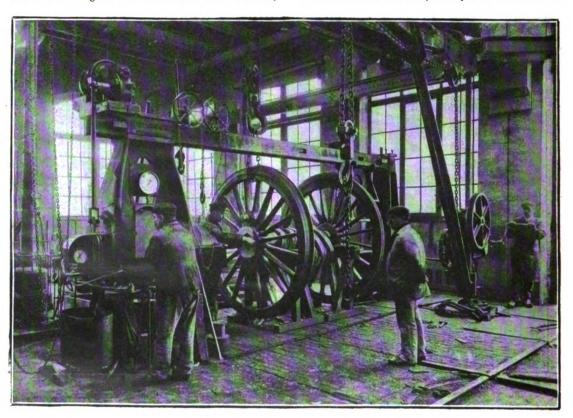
PRESSE A CALER LES ESSIBUX DES MACHINES.
